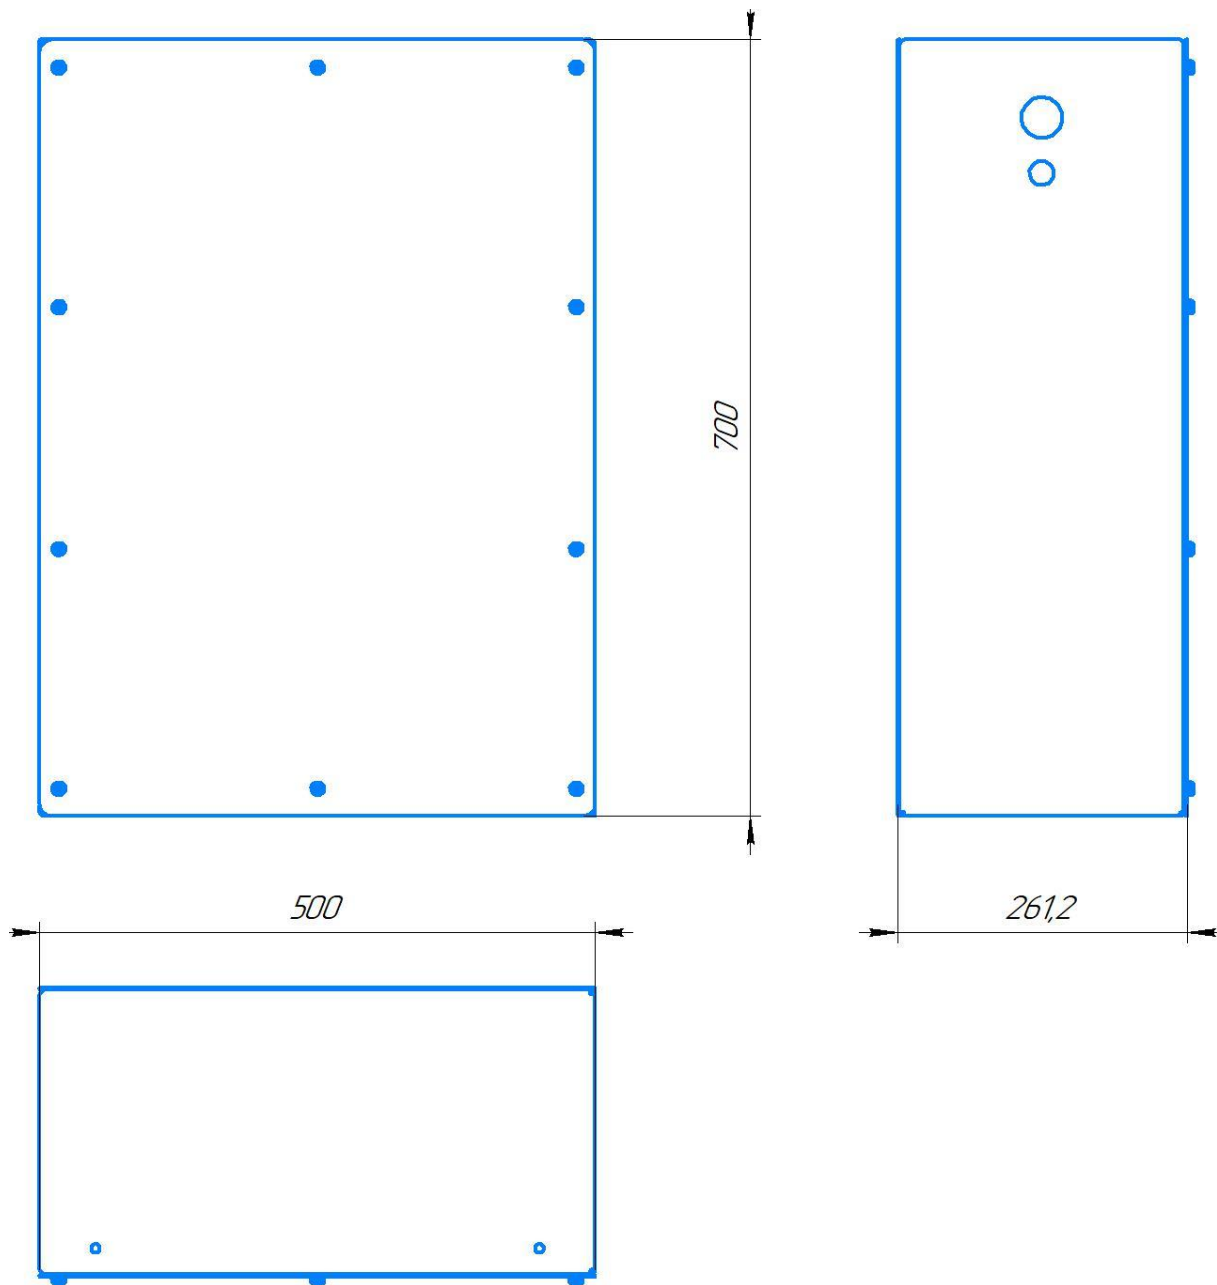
Габаритные и присоединительные размеры БНВ
